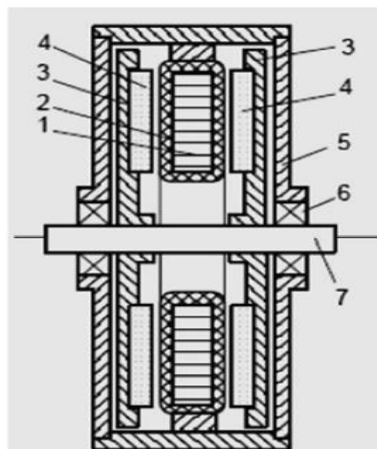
a : Descriptif de la machine à flux axial stator externe
